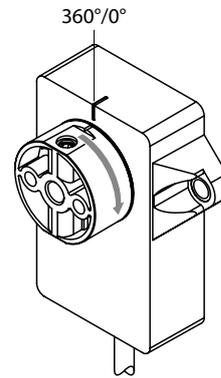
Positionsgeber auf dem Sensorgehäuse ausrichten
